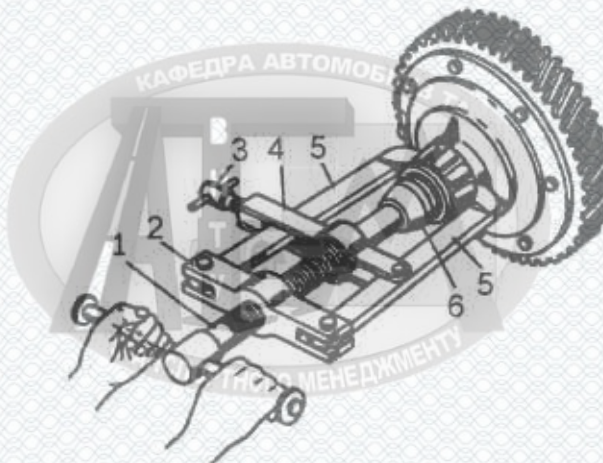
Зняття заднього підшипника з валу ведучої конічної шестерні
